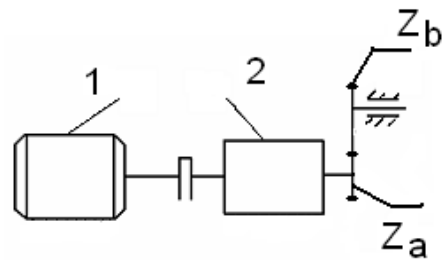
Схема привода: 1-электродвигатель; 2-планетарный редуктор; Z_a , Z_b - зубчатые колеса
